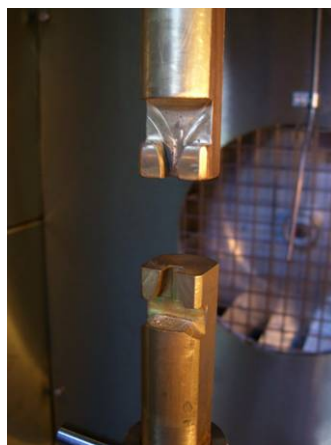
Probenkörper nach dem Zugversuch (markiert Fläche Spannbacken)
